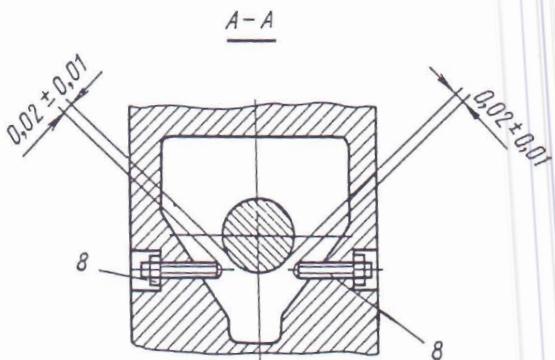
Шпиндель шлифовальной головки станков ЗЕ711В, ЗЕ721В-І, ЗЕ721ВФІ-І, ЗЕ711В-І
